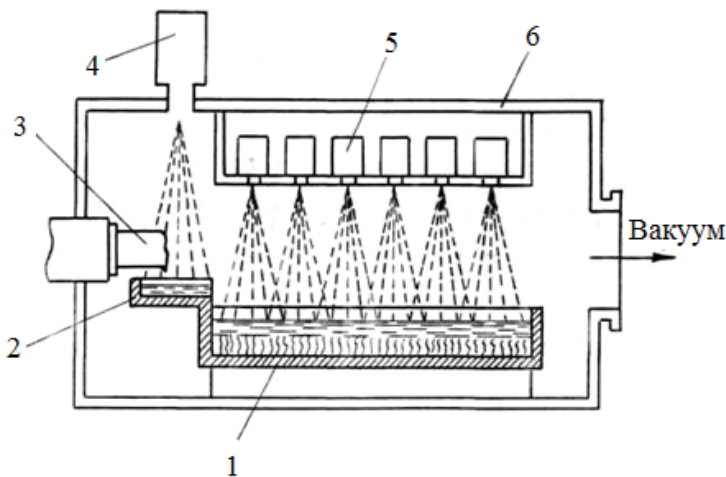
Схема установки ЭЛП с промежуточной емкостью и холодным подом: 1 — горизонтальный кристаллизатор; 2 — промежуточная емкость; 3 — переплавляемая заготовка; 4 — электронно-лучевая пушка для расплавления заготовки и нагрева металла в промежуточной емкости; 5 — электронно-лучевые пушки для нагрева металла на холодном поду; 6 — корпус печи
